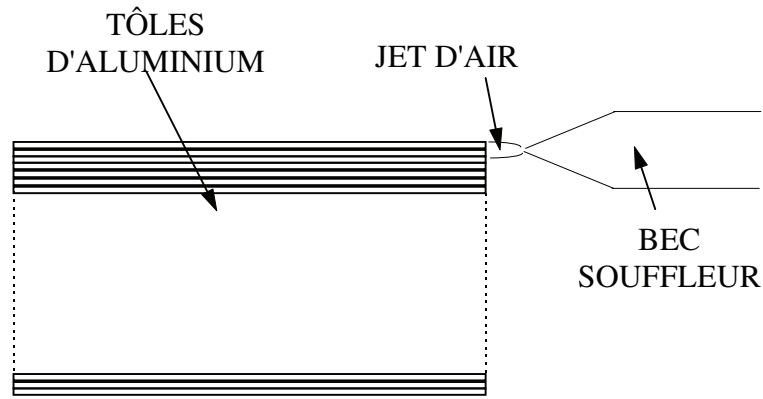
Vue en coupe du système de dépilage de tôles par jet d'air
